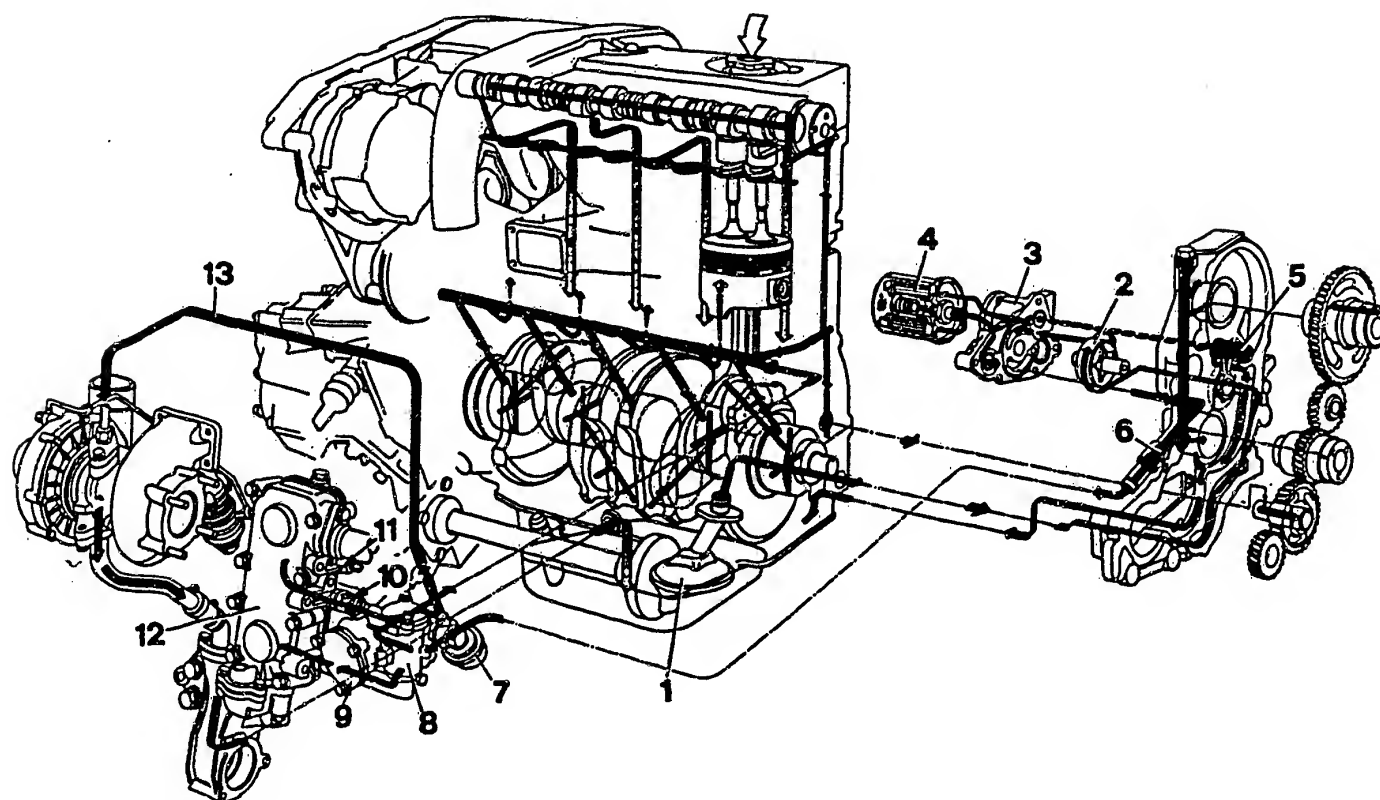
Motor 2500 turbo ds: Ölkreislauf mit 1 Ansaugsieb – 2 Ölpumpe – 3 Filtergehäuse – 4 Ölfiler im Hauptstrom – 5 Überdruckventil – 6 Zufuhrleitung – 7 Öldruckgeber – 8 Ölthermostat – 9 Zusatzfilter – 10 Öldruckschalter – 11 Öltemperaturgeber – 12 Wasser-Öl-Wärmetauscher – 13 Zufuhrleitung zum Turbolader.
